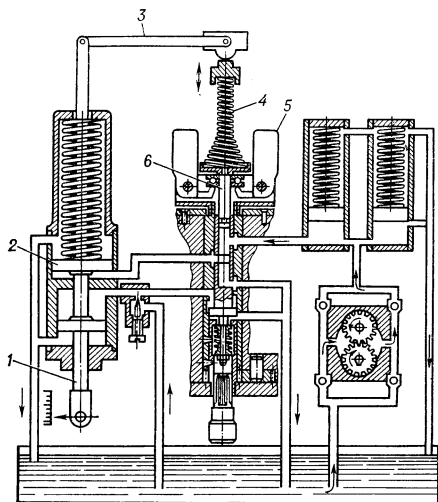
Центробежный регулятор непрямого действия: 1 — шток; 2 — поршень; 3 — рычаг обратной связи; 4 — пружина; 5 — груз; 6 — золотник.
